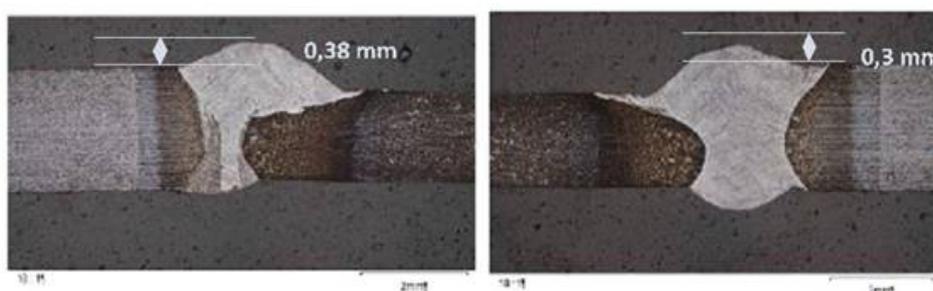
Exemplo de macrografia de cordões de soldadura híbrida laser – MAG para a geração de componentes multimaterial do tipo TWB em aços para estampagem a quente
